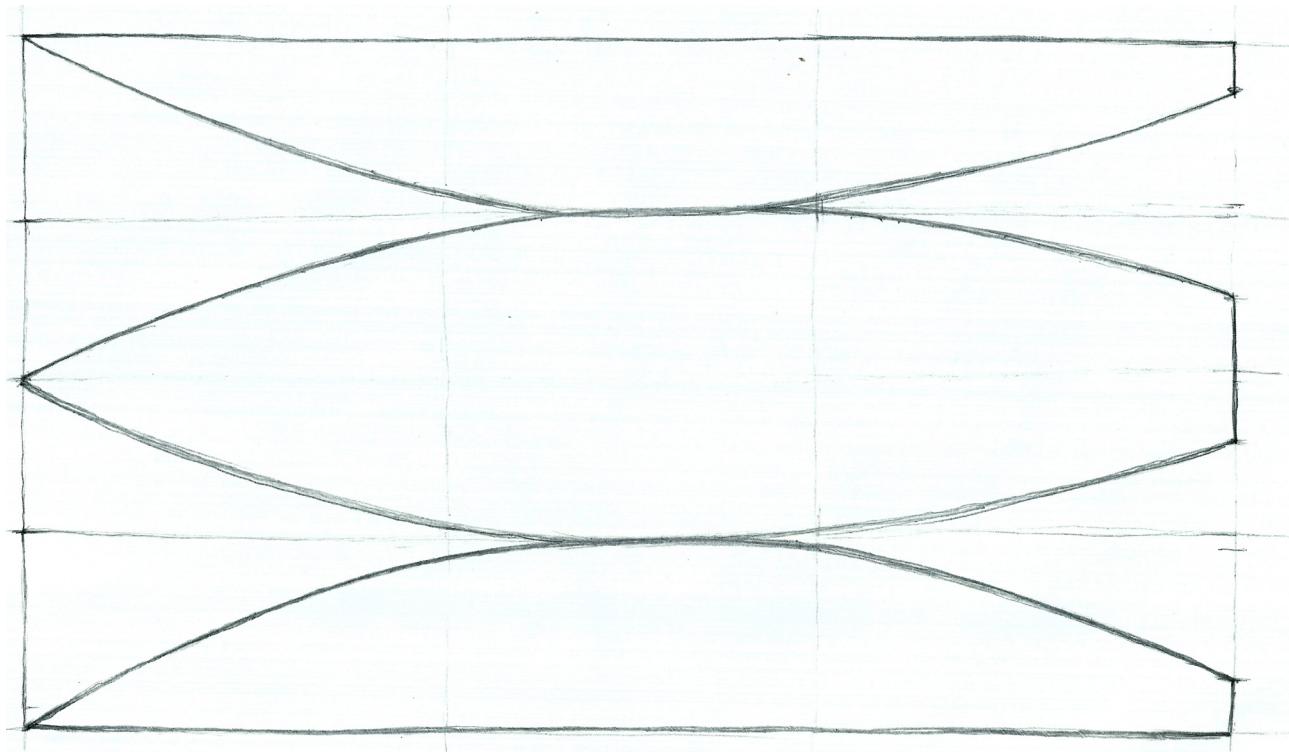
Grundriss Bodenplatte und Seitenteile
